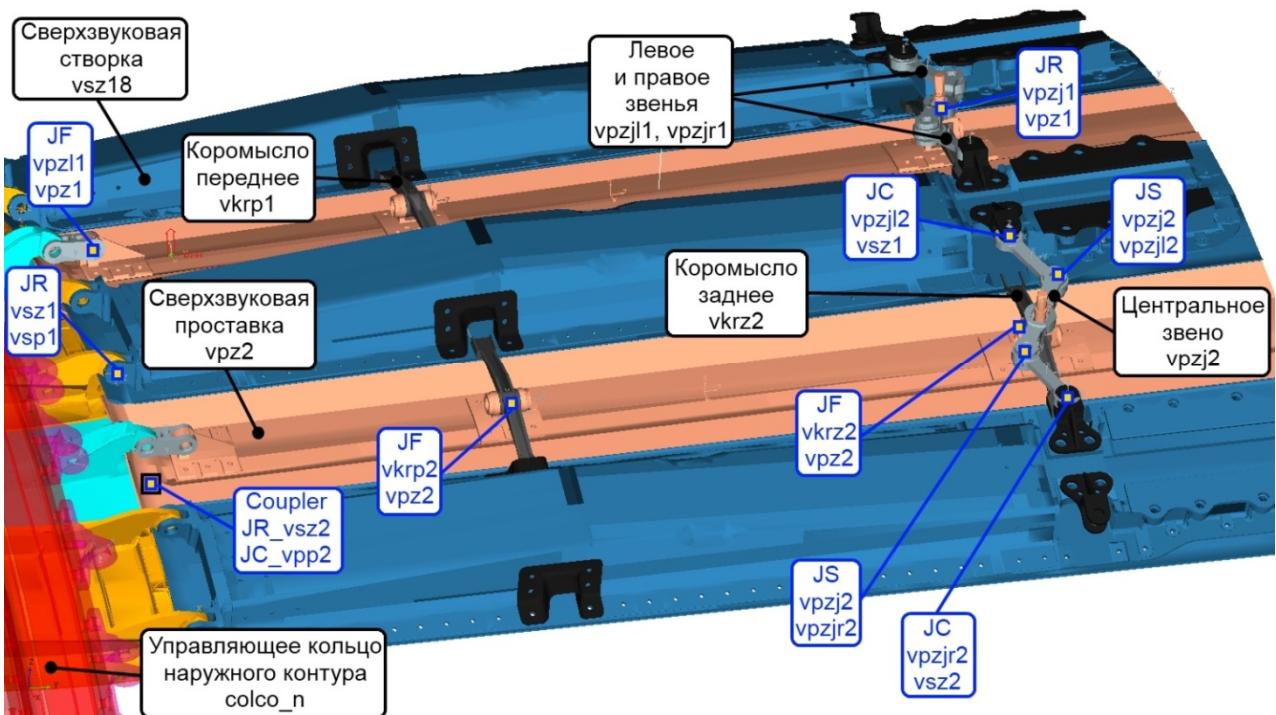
Вид 3D-модели с обозначениями (внутренний контур, зона сверхзвуковых створок)
